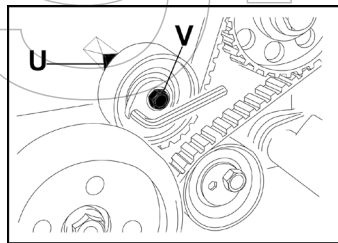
Agendo sul tenditore T2, portare l'indicatore mobile U nella posizione di tensione, serrare quindi il dado di fissaggio V.
